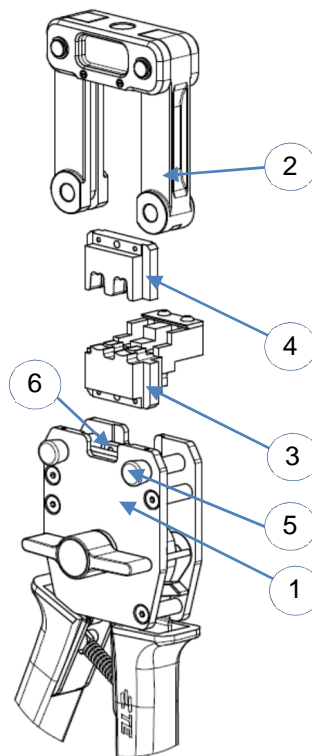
Explosionszeichnung (Darstellung kann abweichen)
